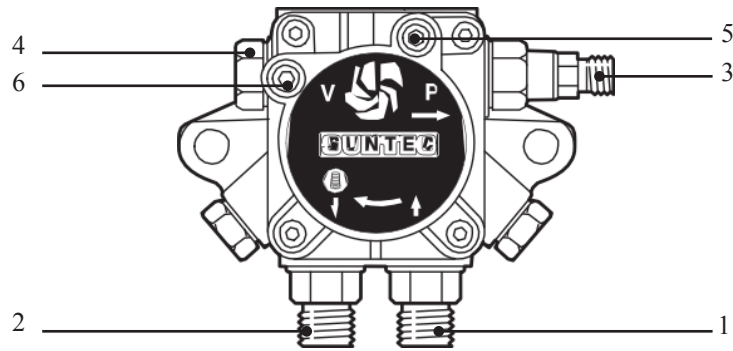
Насос шестеренчатый жидкотопливный марки АЕ
